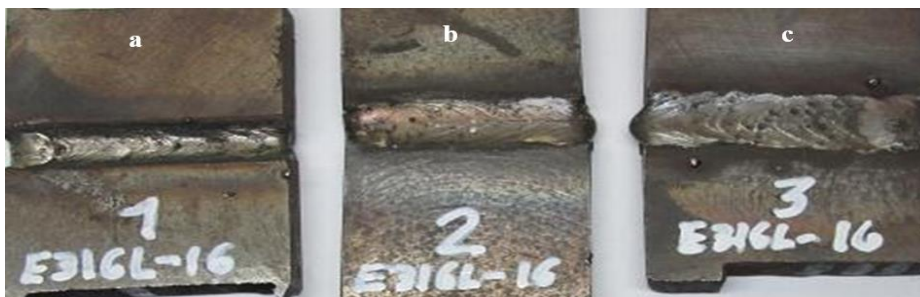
Muestras soldadas con electrodos E 316L-16.
